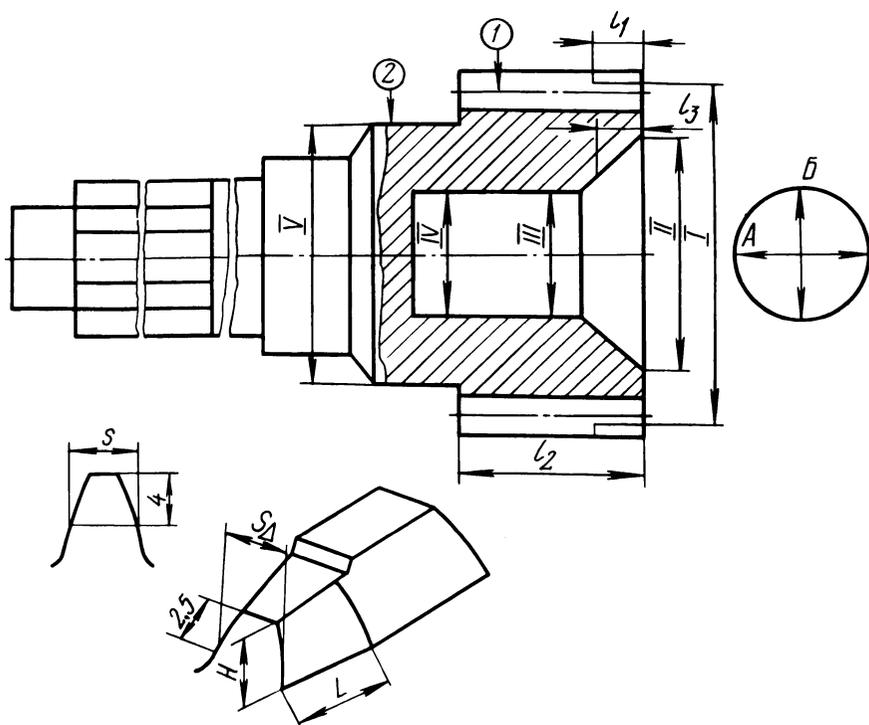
Схема замеров основных параметров вала-шестерни 51-7017: I — диаметр замковой части венца; II — наружный диаметр внутреннего конуса; III, IV, V — диаметры посадочных поверхностей подшипников;  $l_1$  — длина скоса замковой части;  $l_2$  — длина зуба; S,  $S_\Delta$  — соответственно толщина зуба по делительной окружности неизношенной и изношенной части зуба; LH — соответственно длина и высота изношенной части зуба; 1, 2 — соответственно места замеров радиального боения замковой части зуба и посадочной поверхности под подшипник.
